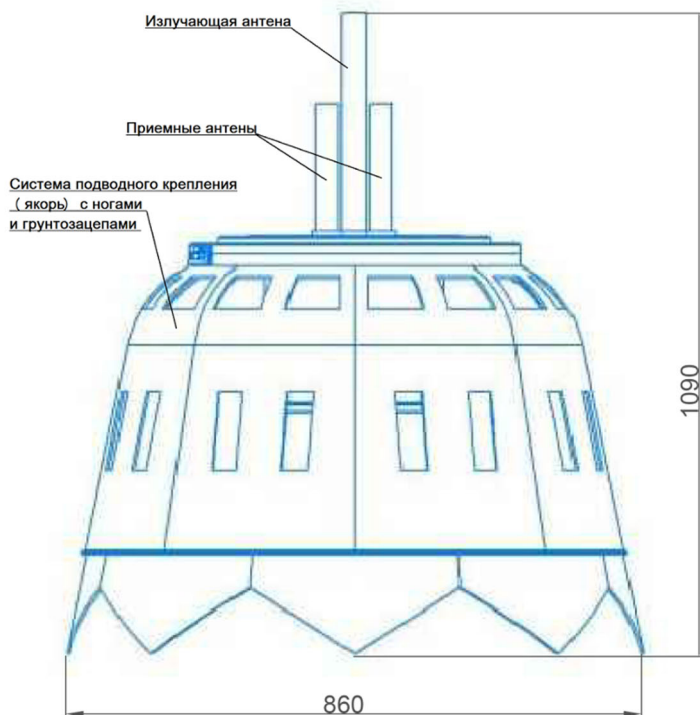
Габаритный чертёж СОПП серии М
